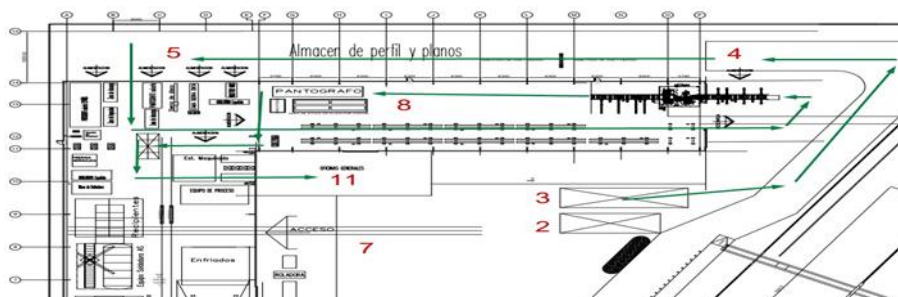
Layout mejorado 2 de la Planta Durosa Santa Rosa SA, de CV.
